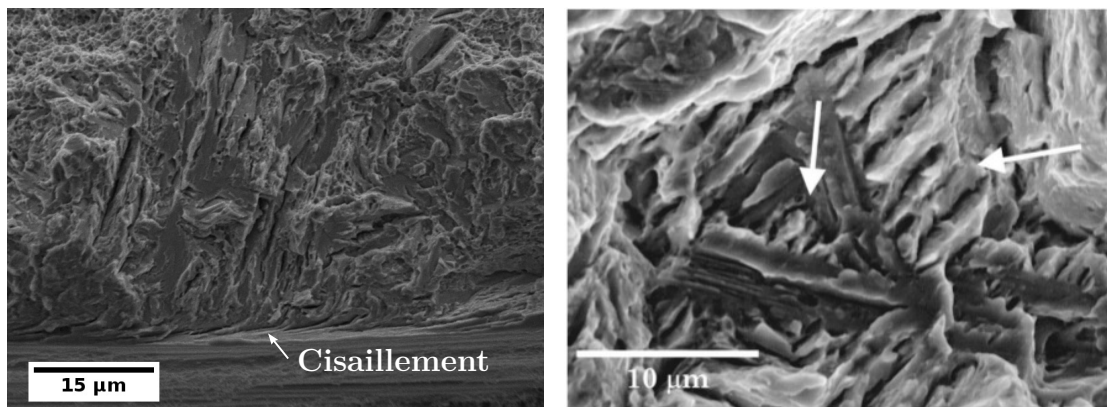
Fractographies des éprouvettes AL et AE
